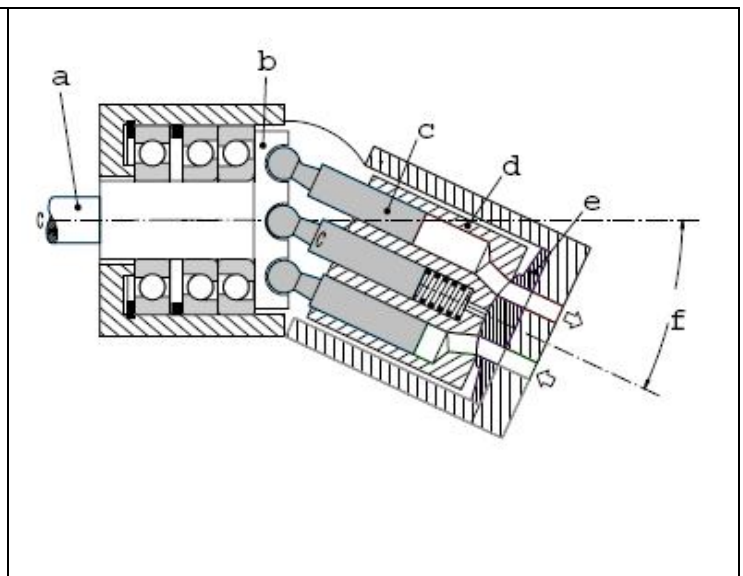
Схема осевого поршневого насоса (а: вал двигателя; б: приводной диск; с: поршни, d: цилиндр; e: регулирующая пластина; f: регулирующий угол).
